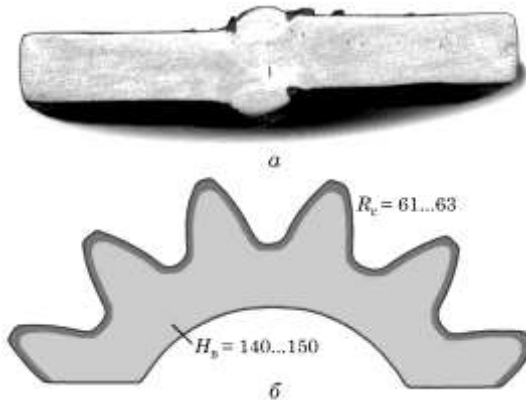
Макроструктура поверхні: а — зварного шва; б — шестерні
